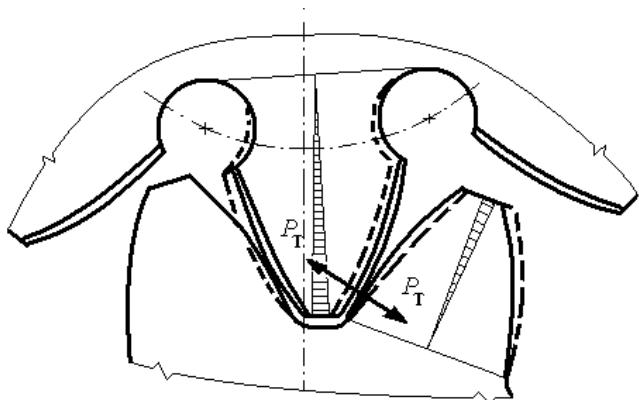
Эпюры изгибов зубьев шевера и обрабатываемого колеса под действием тангенциальной силы
